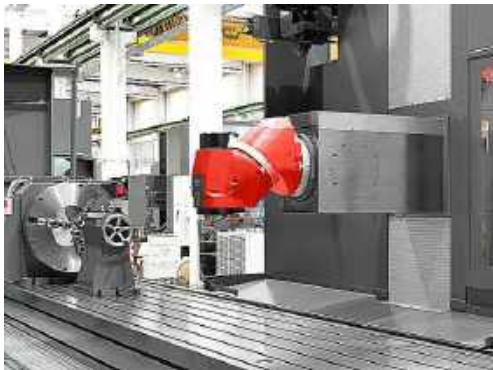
Групова фрезерна обробка рам візка шасі пасажирського літака
